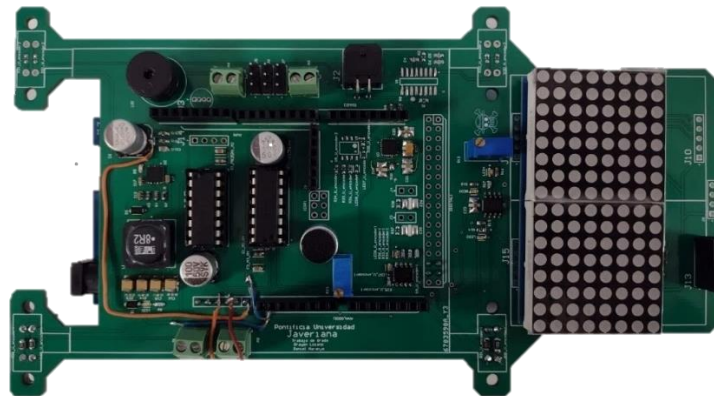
Vista superior del PCB Versión 2 con componentes soldados
